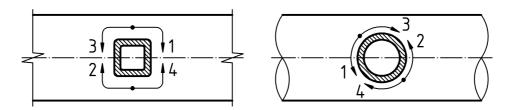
Positions de départ et d'arrêt et séquence de soudage
